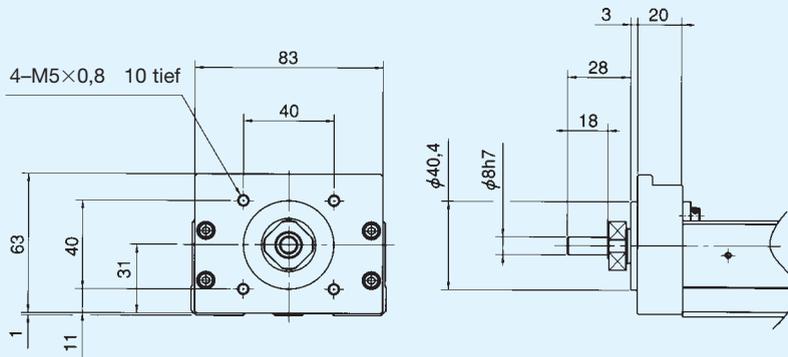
KR46 Housing A ohne Motorflansch (Kennziffer □ □ 60)
